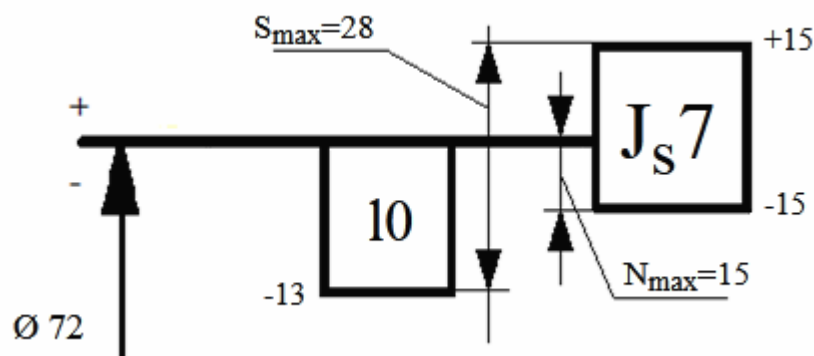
Поля допусков и показатели точности посадки для сопряжения наружного кольца подшипник с отверстием корпуса
